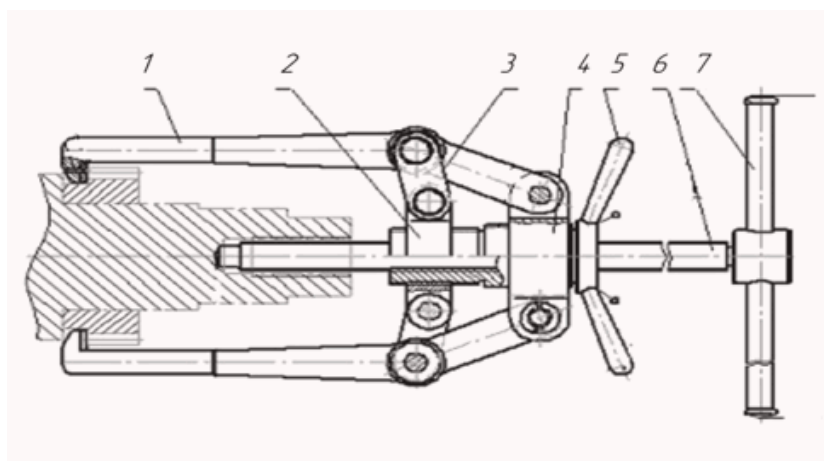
Рис. 4. Універсальний знімач підшипників мод. ЛІСОТА АТВ-1131АТВ: 1 – захват; 2 – основний корпус; 3 – упор; 4 – регульовальна головка; 5 – регульовальна ручка; 6 – болт подачі; 7 – ручка подачі
